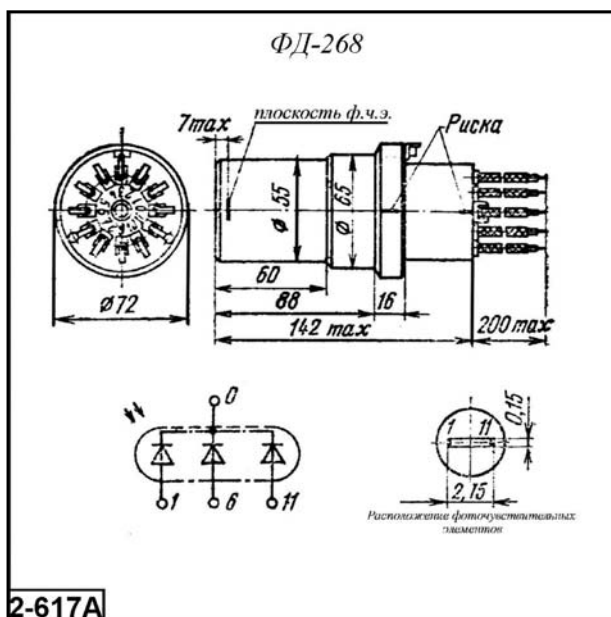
Внешний вид и габаритные размеры охлаждаемого фотодиода ФДО-268
